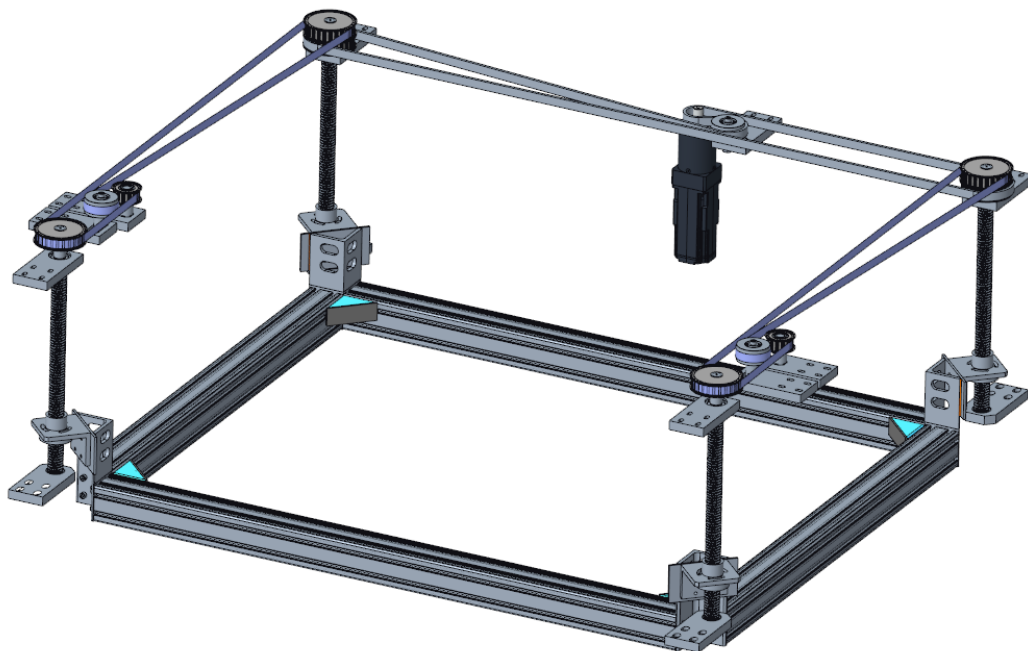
Konstrukce s dlouhým řemenem bez stroje
